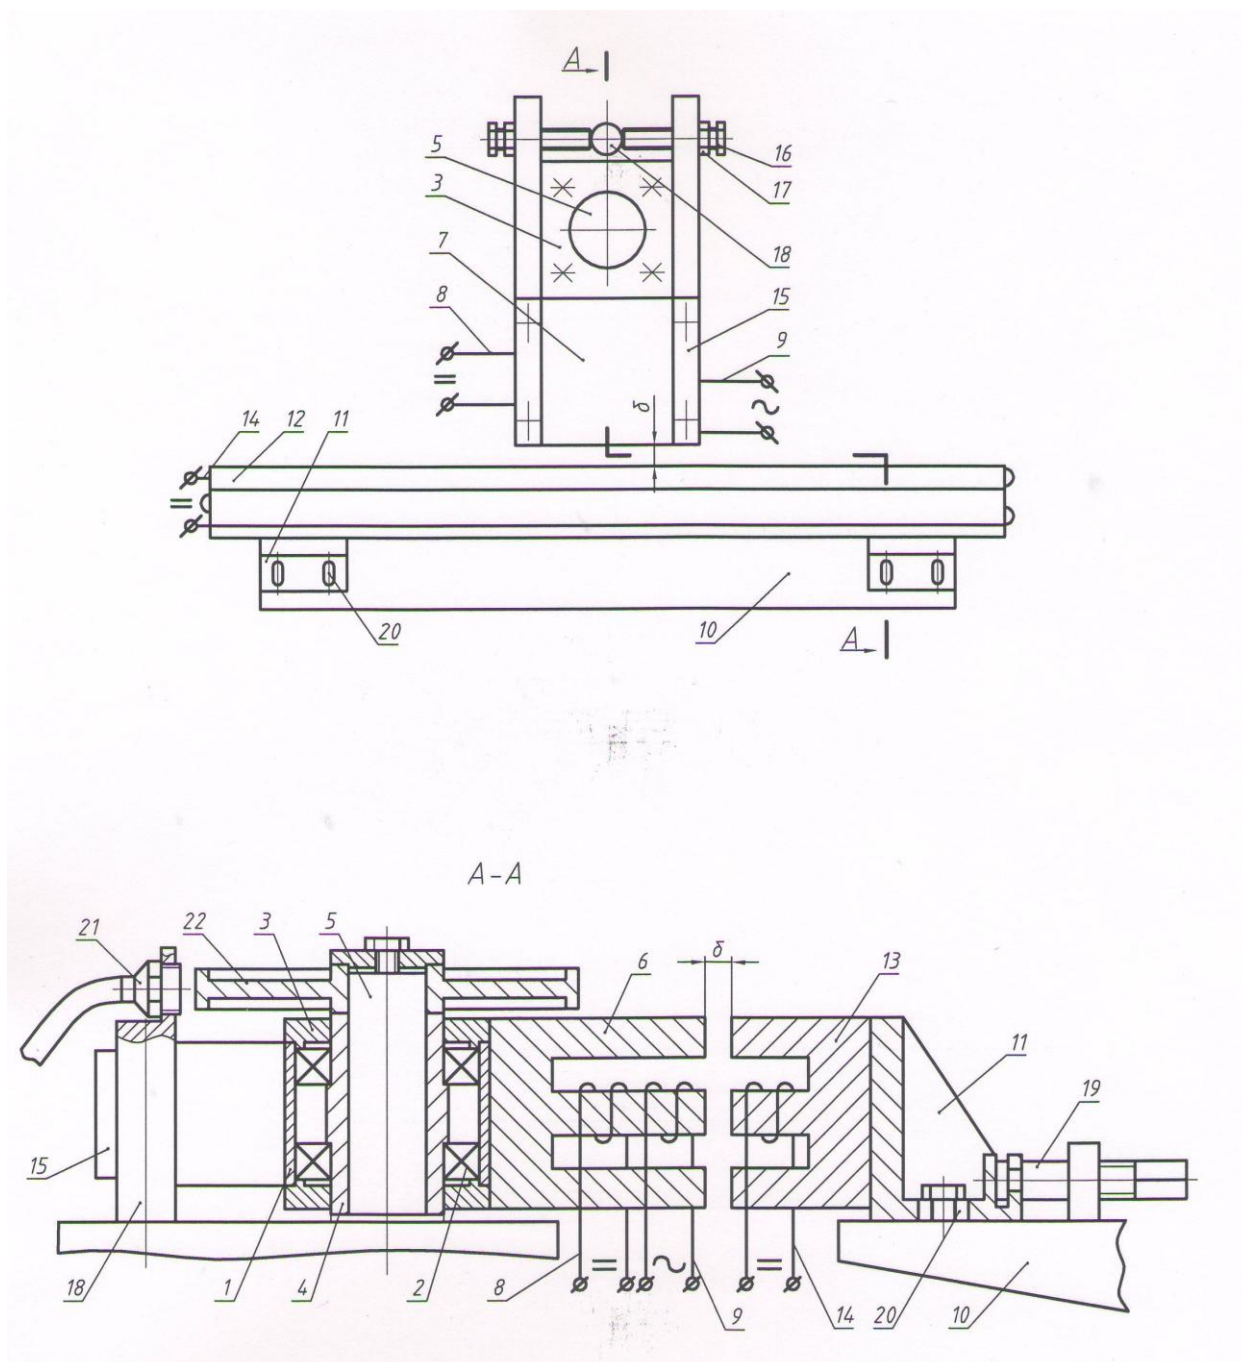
Нагрузочное устройство для испытаний фрезерных станков.
